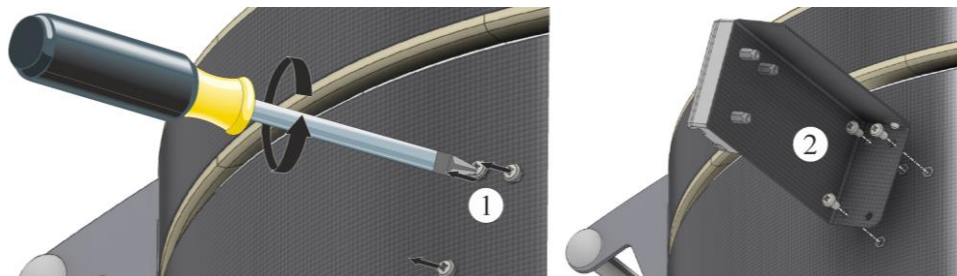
Монтаж держателя на корпусе печи (рисунок примерный)
